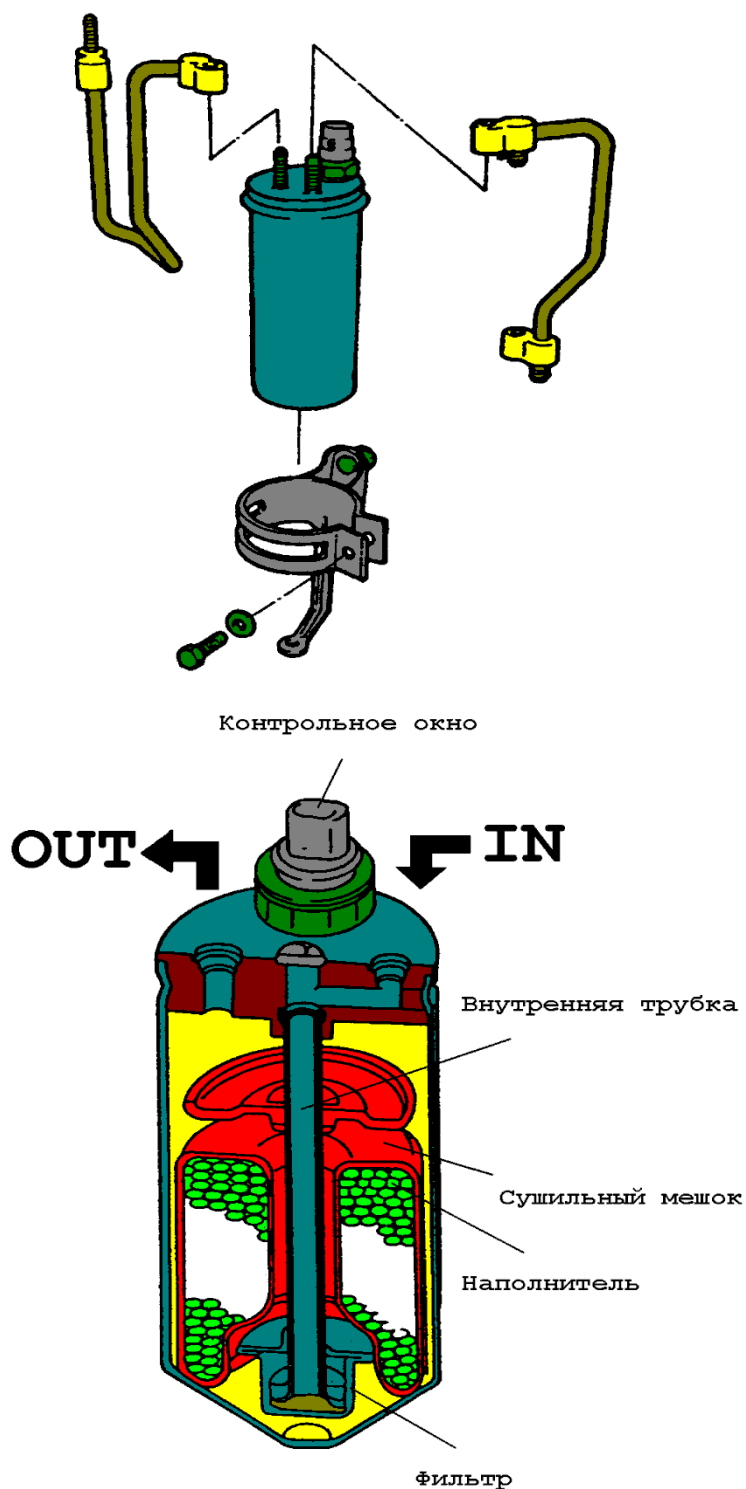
Загальний вигляд типового ресиверу/осушувача.
